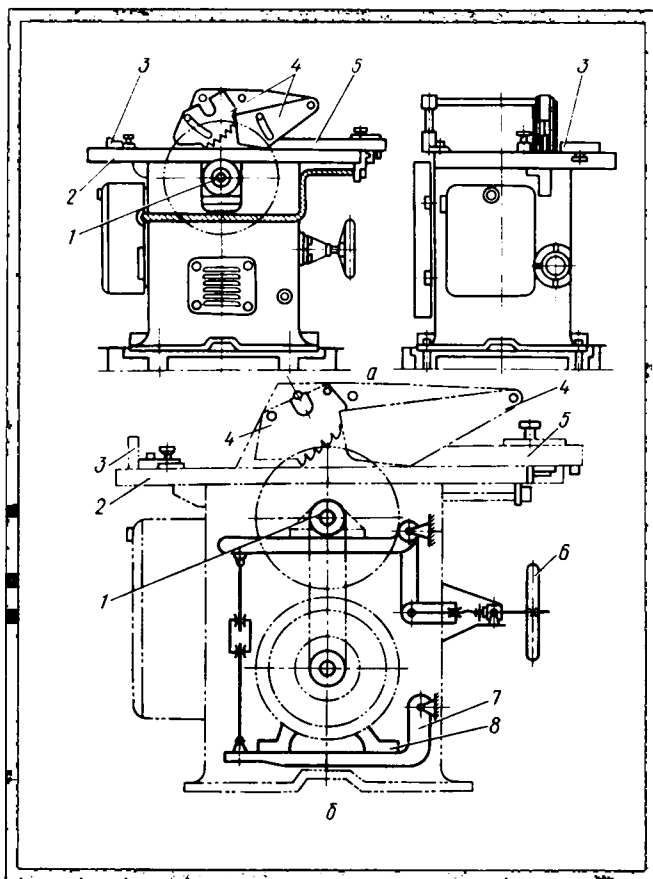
Универсальный круглопильный станок ЦБ-2:
